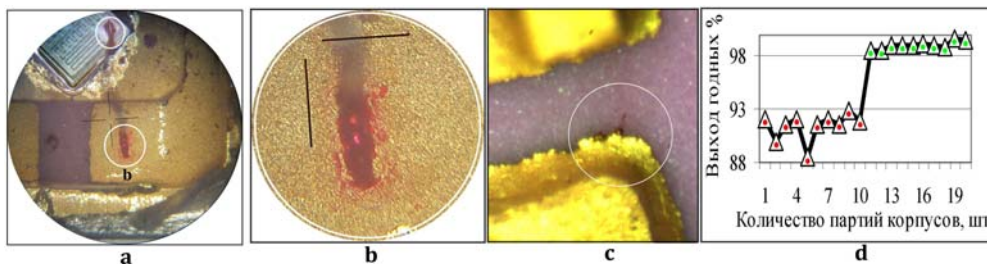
Выявление родамина в металлокерамическом соединении (а), (b – увеличено), (с) и динамика выхода годных по герметичности (d) для разного тока сварки (80 А для партий № 1-10 и 65А для партий № 11-20)
